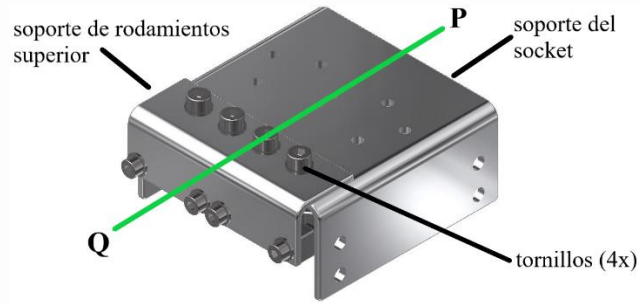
Ensamblaje entre el soporte del socket y el soporte de rodamientos superior.
